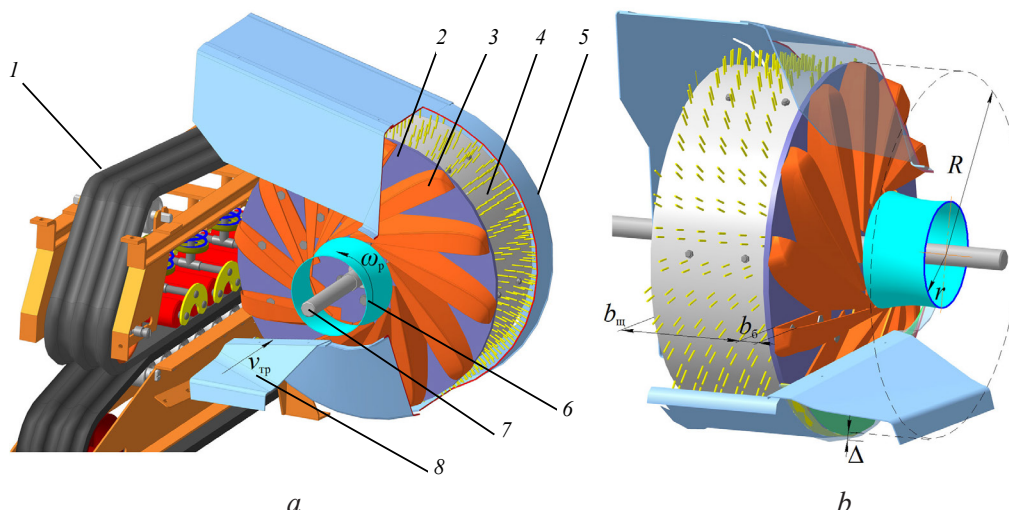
Конструкция роторного бильно-вычесывающего устройства: *a* – общий вид устройства (*1* – зажимной транспортер; *2* – ротор; *3* – бичи; *4* – вычесывающе-транспортирующая щетка; *5* – кожух; *6* – кольцо; *7* – вал ротора; *8* – стол); *b* – общий вид ротора.
